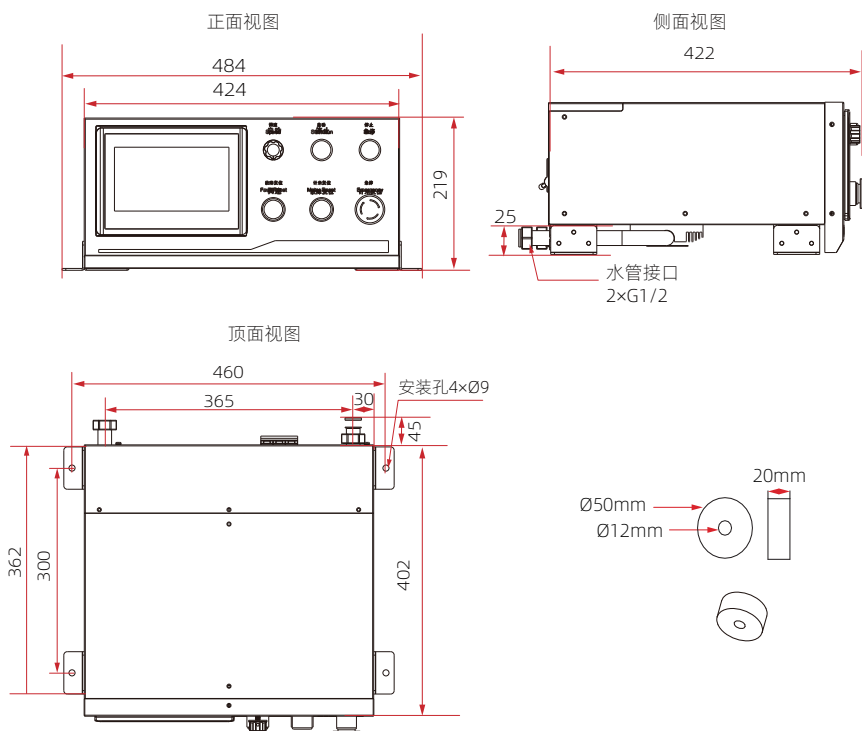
（一体液冷 - 后出冷却管）外型尺寸安装尺寸及减震垫示意图（AWD100-4T0501~AWD100-4T1804）（单位：mm）
